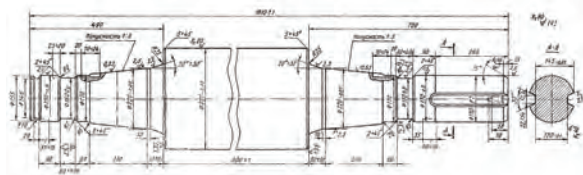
Схема валка рабочей клетки 350х600 сортового стана 350
